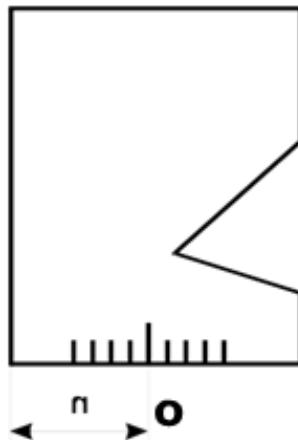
Точка О выхода луча, отмеченная на боковой поверхности корпуса ПЭП
